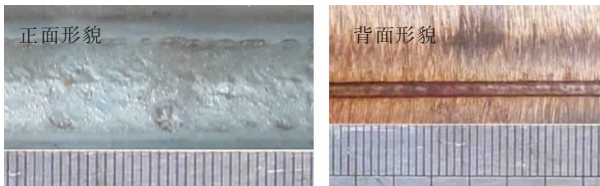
8 mm 厚低碳钢板 DP-TIG 焊接形貌
